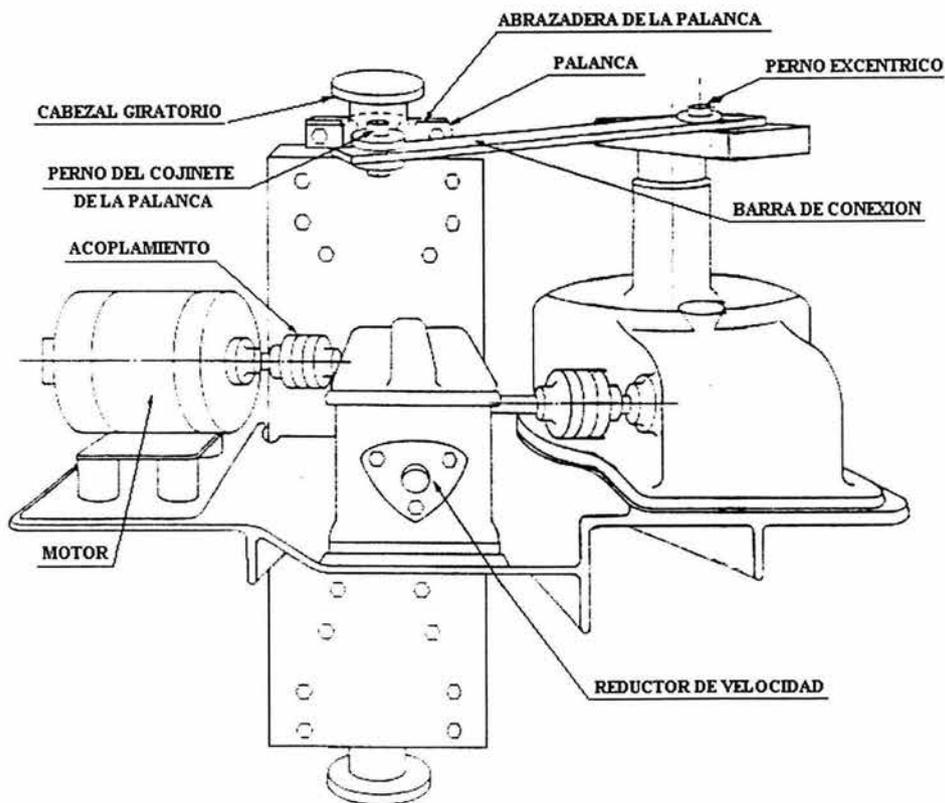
Unidad motriz del dispositivo limpiador (soplador de hollín).
